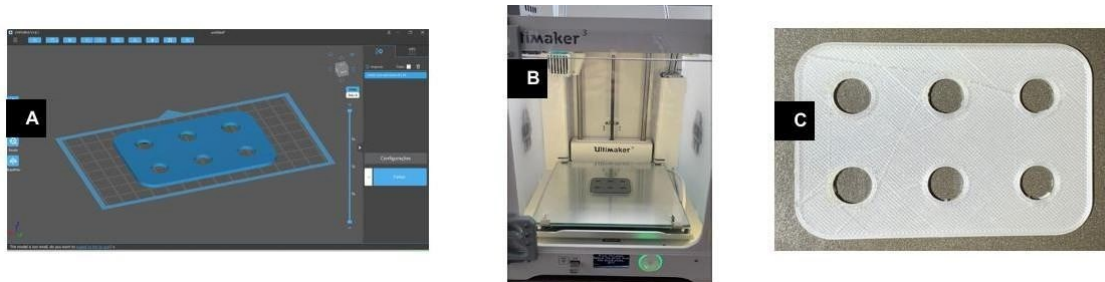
Confeção de molde para os provetes de resina convencional: A - desenho CAD; B - Impressora 3D (Ultimaker 3); C - Molde impresso em PLA
